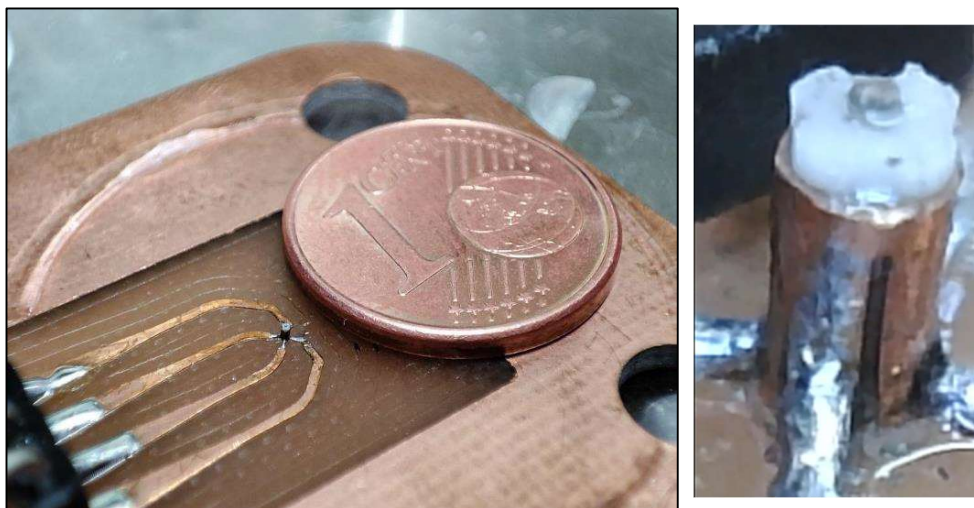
Microactuador 1Fr soldado a una PCB para ensayos.
